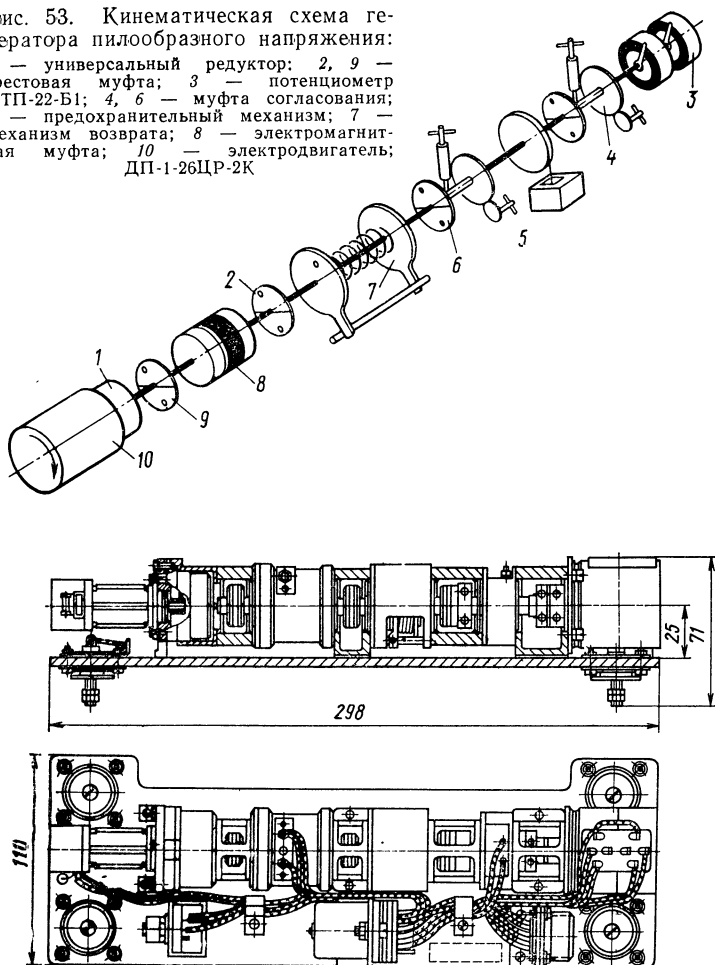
Сборочный чертеж генератора пилообразного напряжения
